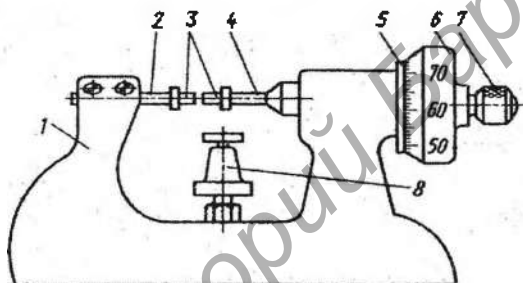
Микрометр настольный МН: 1 — корпус, 2 — пятка, 3 — измерительные стержни, 4 — микровинт, 5 — стебель, 6 — барабан, 7 — трешотка [10, с. 162]
